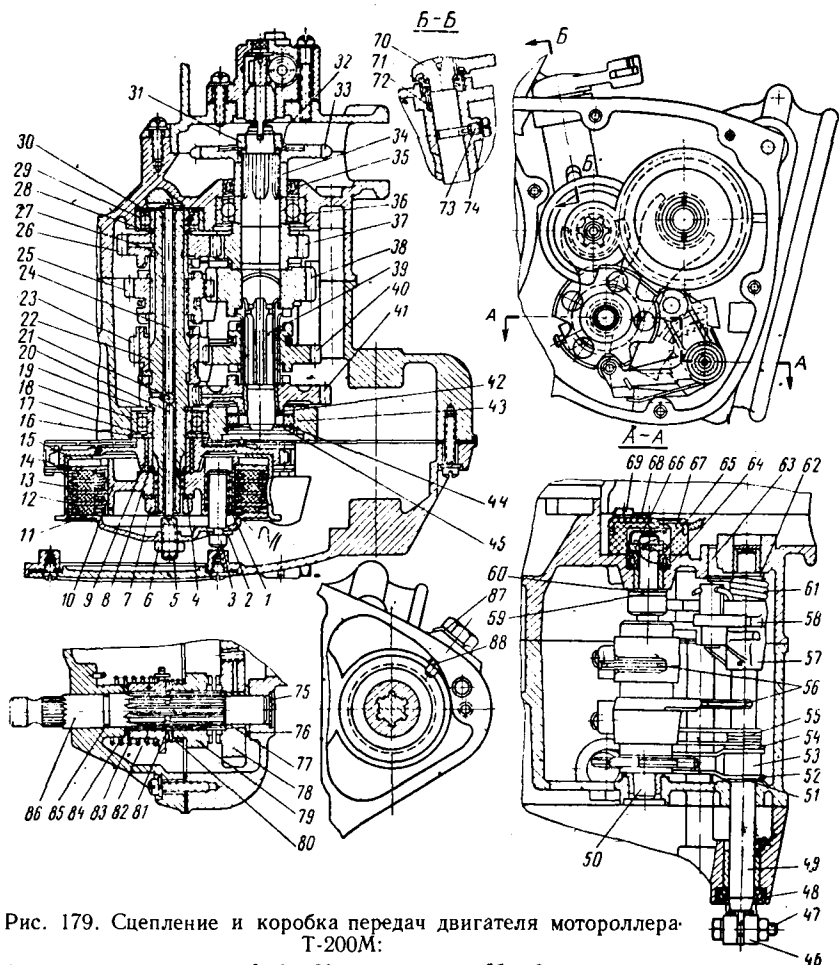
Сцепление и коробка передач двигателя мотороллера Т-200М:
